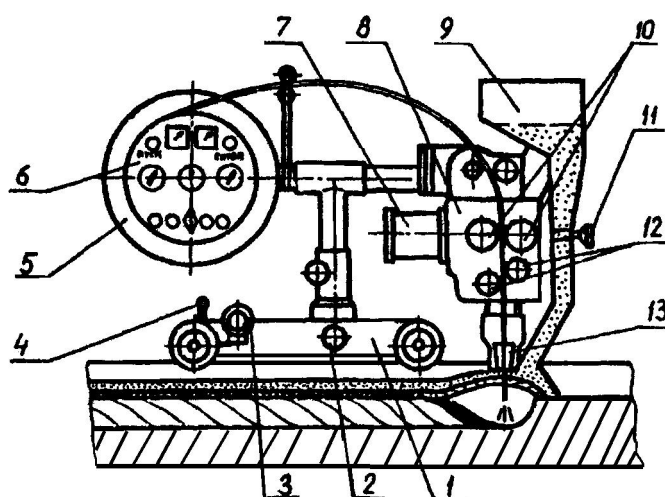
Схема технологического процесса автоматической сварки под флюсом
